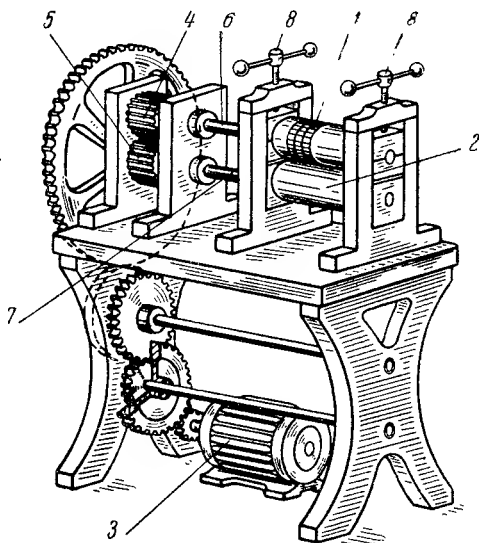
Двухвальный прокатный стан для изготовления ленты из припоев
